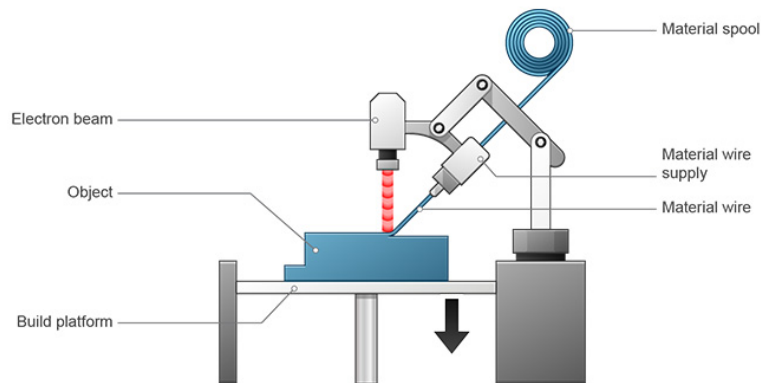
Partes de una máquina de fabricación DED que usa haz de electrones como fuente de energía. [11]
